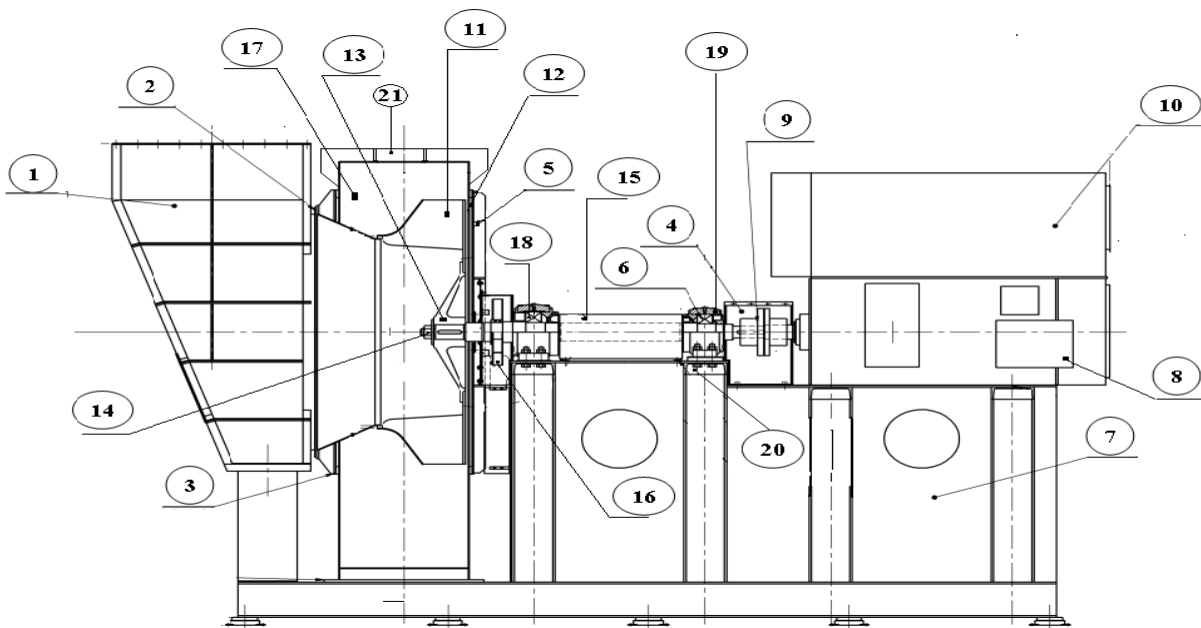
Dessin d'ensemble du ventilateur FN280.[8]
